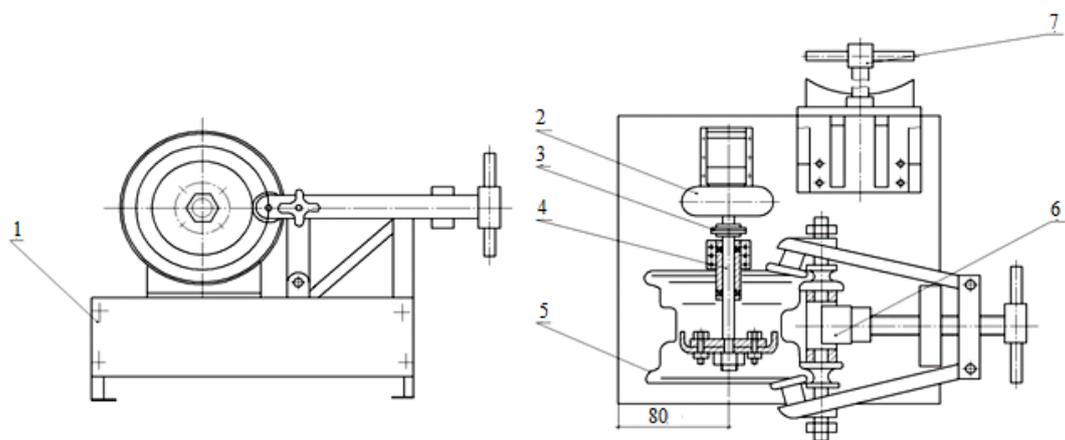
Стенд правки дисков: 1 – станина, 2 – мотор-редуктор, 3 – предохранительная муфта, 4 – ведомый вал, 5 – обрабатываемый диск, 6 – механизм правки, 7 – силовой механизм
